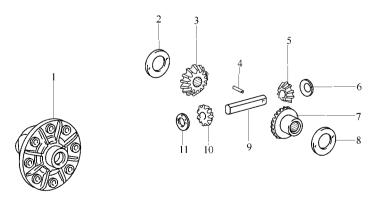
2 小齿轮型式零件分解图 1—差速器壳 2、6、8、11—止推垫圈 3—侧齿轮 4—销子 5、10—差速器小齿轮 7—侧齿轮 9—小齿轮轴
